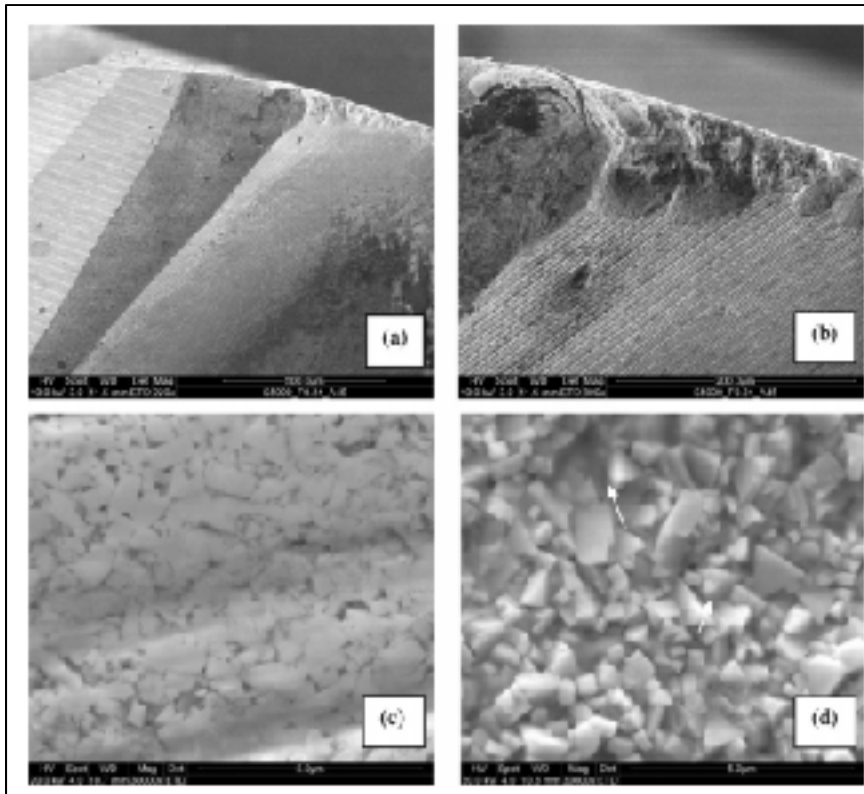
Usure de l'outil lors du détournage a) par abrasion, b) par écaillage, c) nouveau outil et d) fracture des grains de carbure de tungstène (WC) sur un outil utilisé
